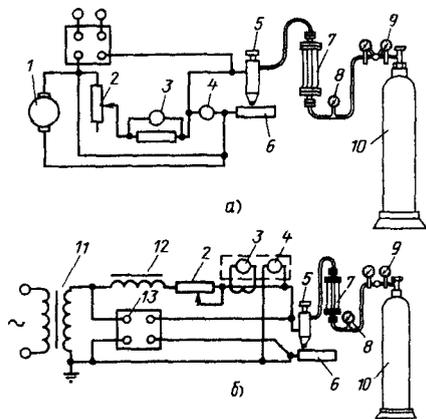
Схемы постов ручной аргондуговой сварки:
